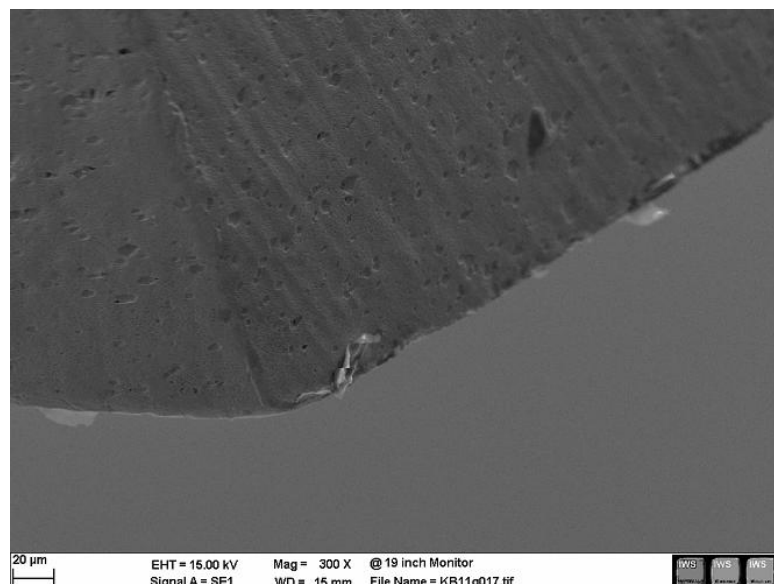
Detail X; Brasseler Standard 440B; unbenützt; REM (300 X)
